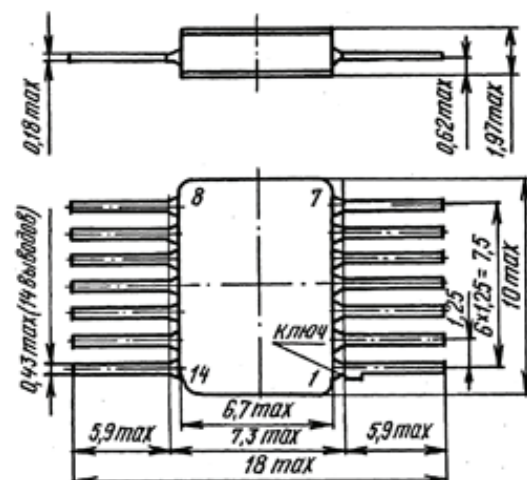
Габаритные чертежи корпусов 401.14-4 и 401.14-5М
